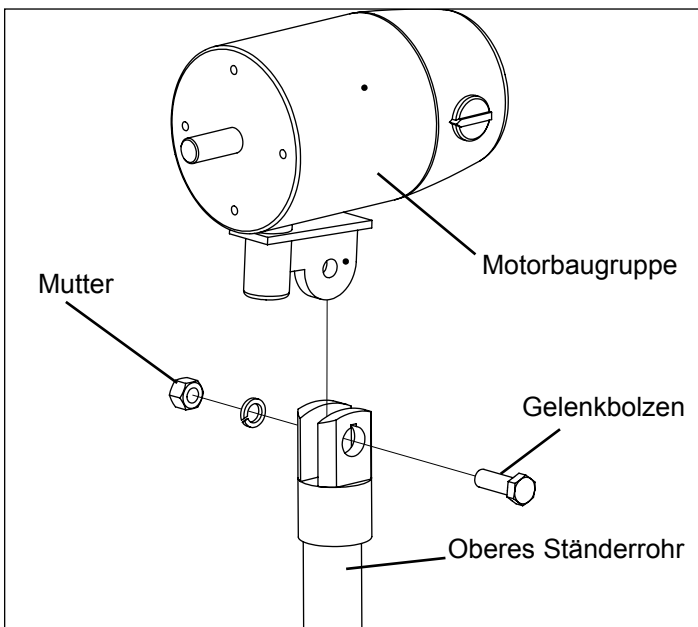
Motor an der Motorträgerbaugruppe befestigen
